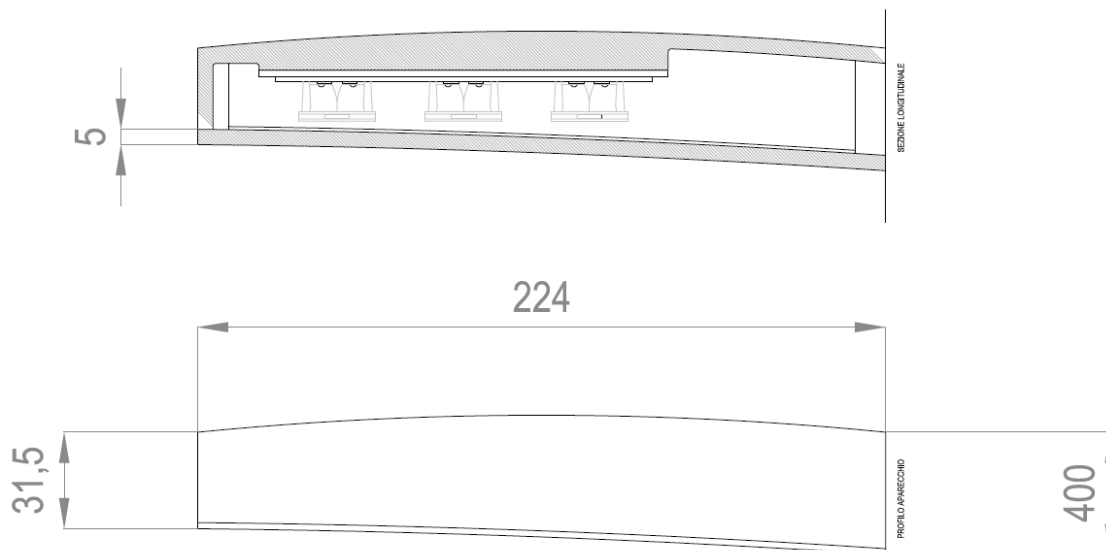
Vista in prospettiva e in sezione del vano ottico a testa palo.
